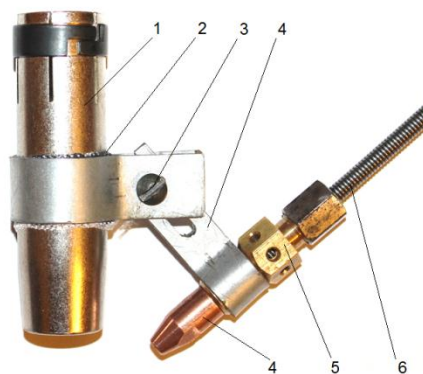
Приспособление для подачи дополнительной холодной электродной проволоки в сварочную ванну
